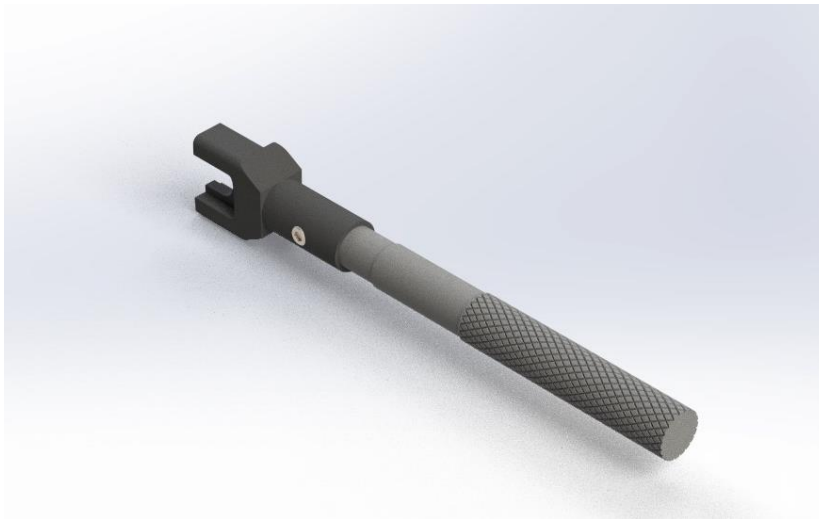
Detail Drawing *Tool Spanner Pull Stud
